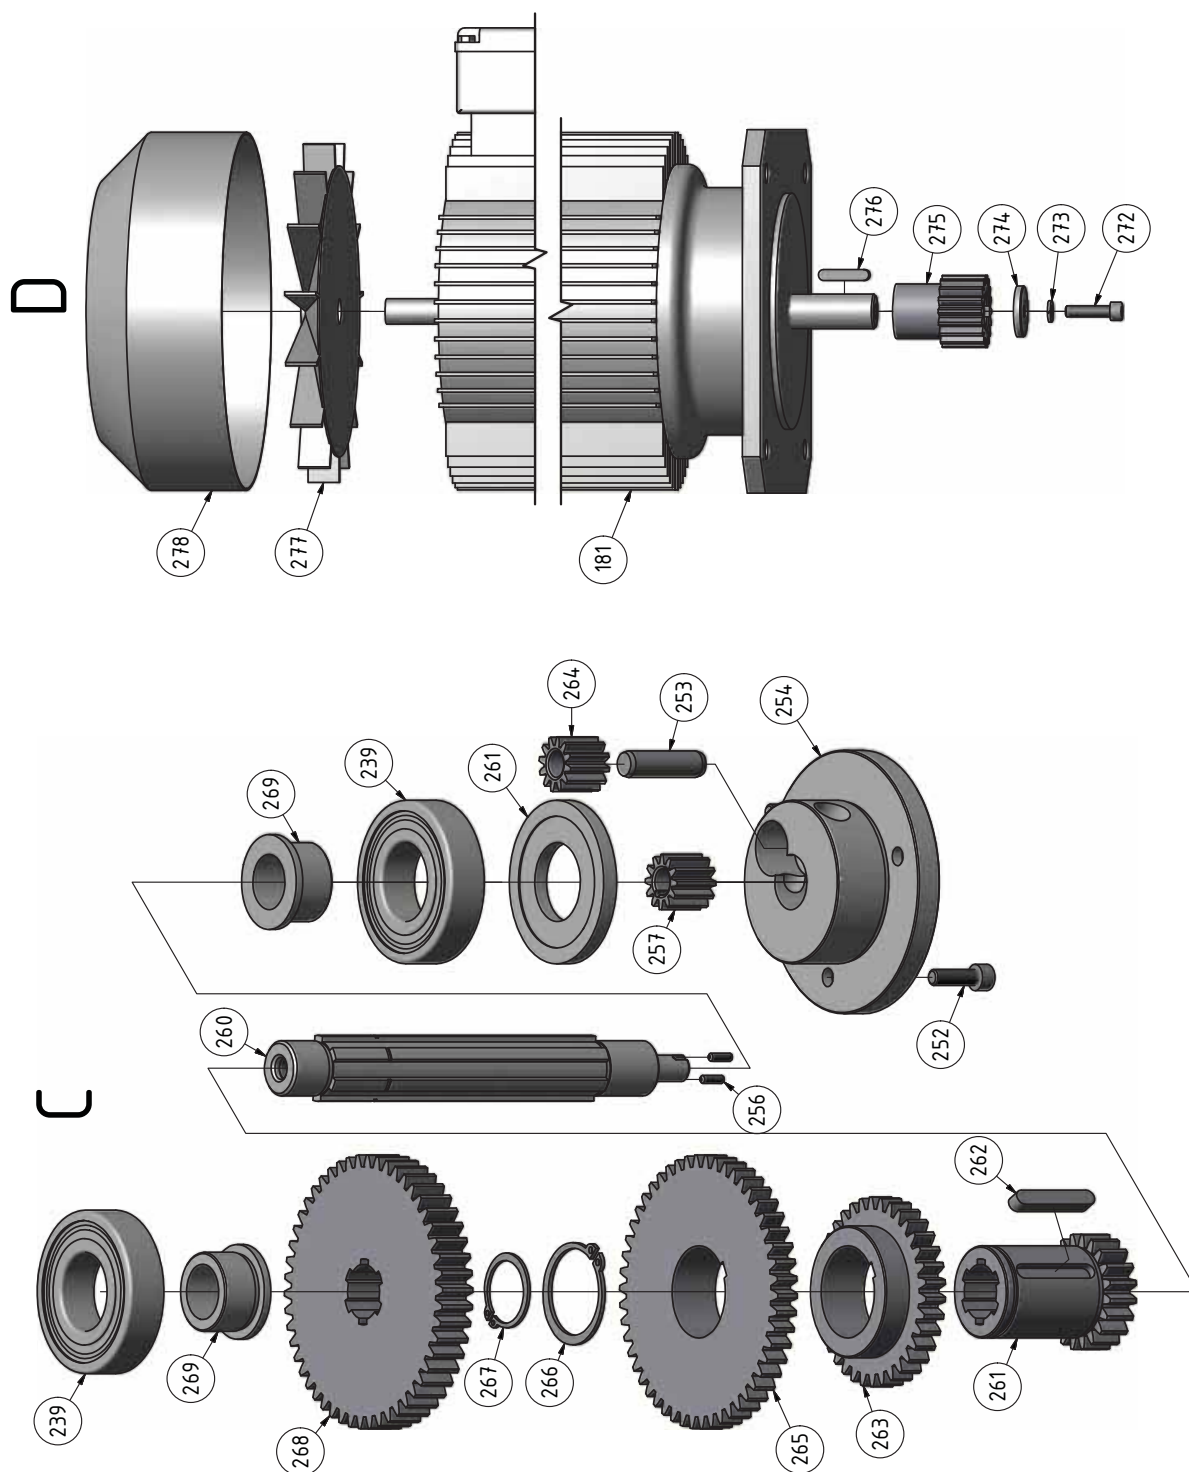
Getriebe Bohrspindel 2 von 4 - Gear box main spindle 2 von 4
